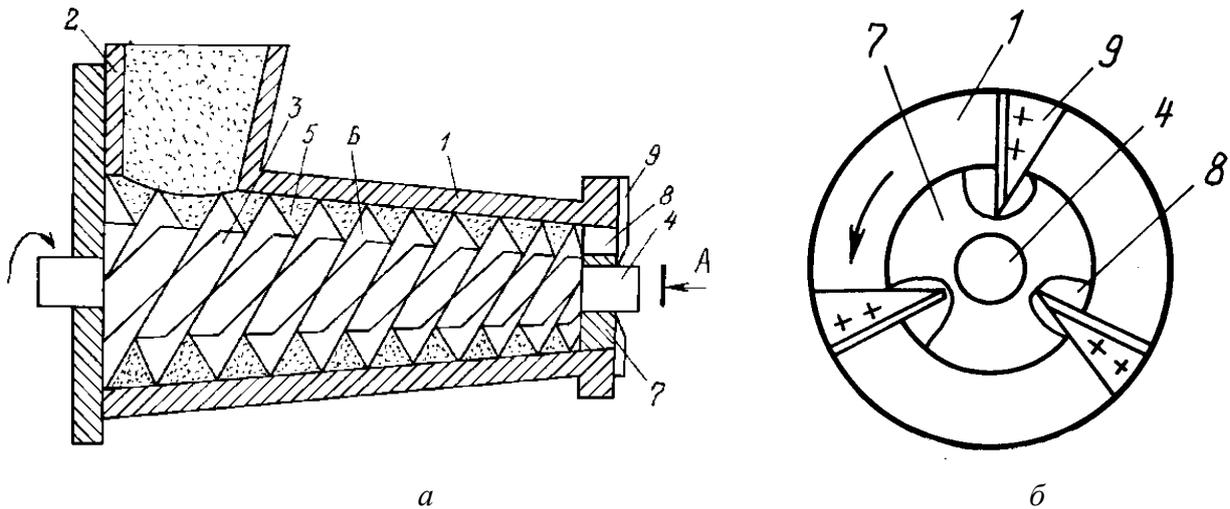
Гранулятор: 1 – корпус; 2 – загрузочный бункер; 3 – поверхность вращения; 4 – вал; 5 – канавки; 6 – однозаходная или многозаходная навивка; 7 – матрица; 8 – отверстия; 9 – ножи
